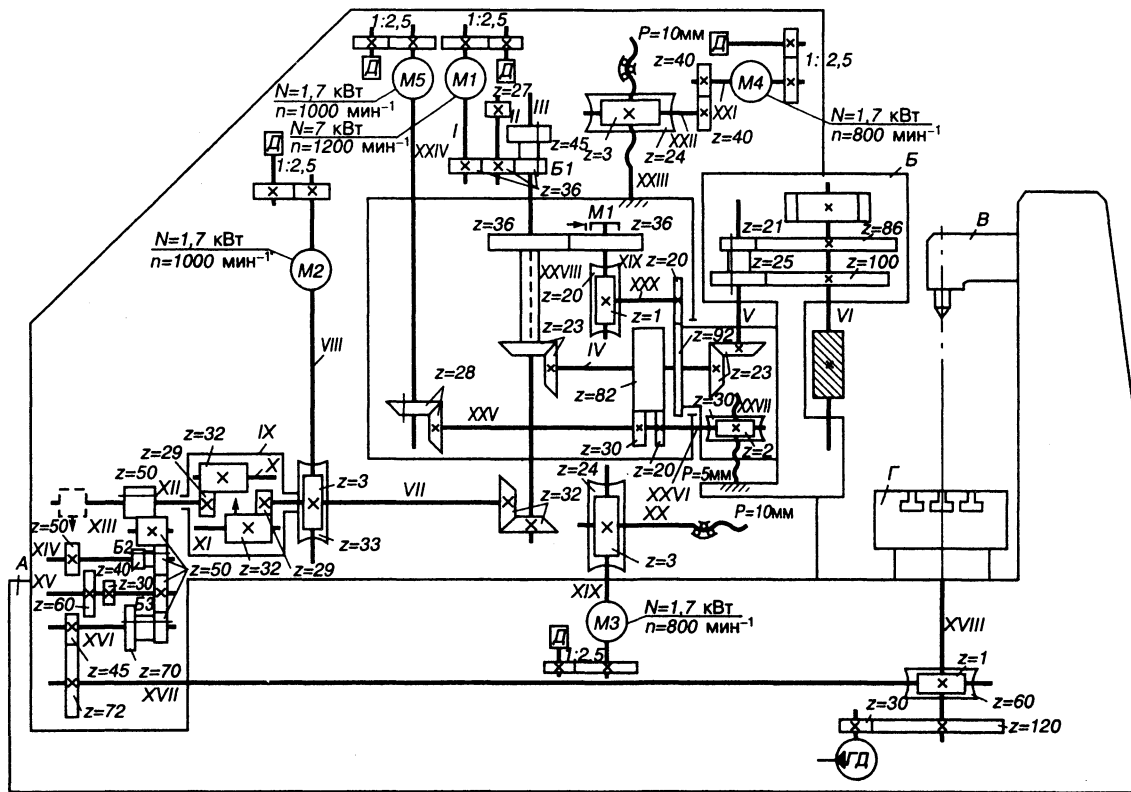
Кинематическая схема зубофрезерного полуавтомата 53А20Ф4 с ЧПУ
